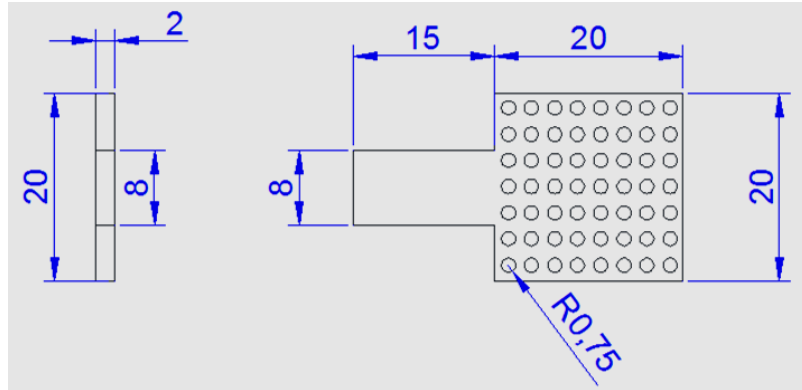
Electrodo para el tratamiento perpendicular (dimensiones en mm).
